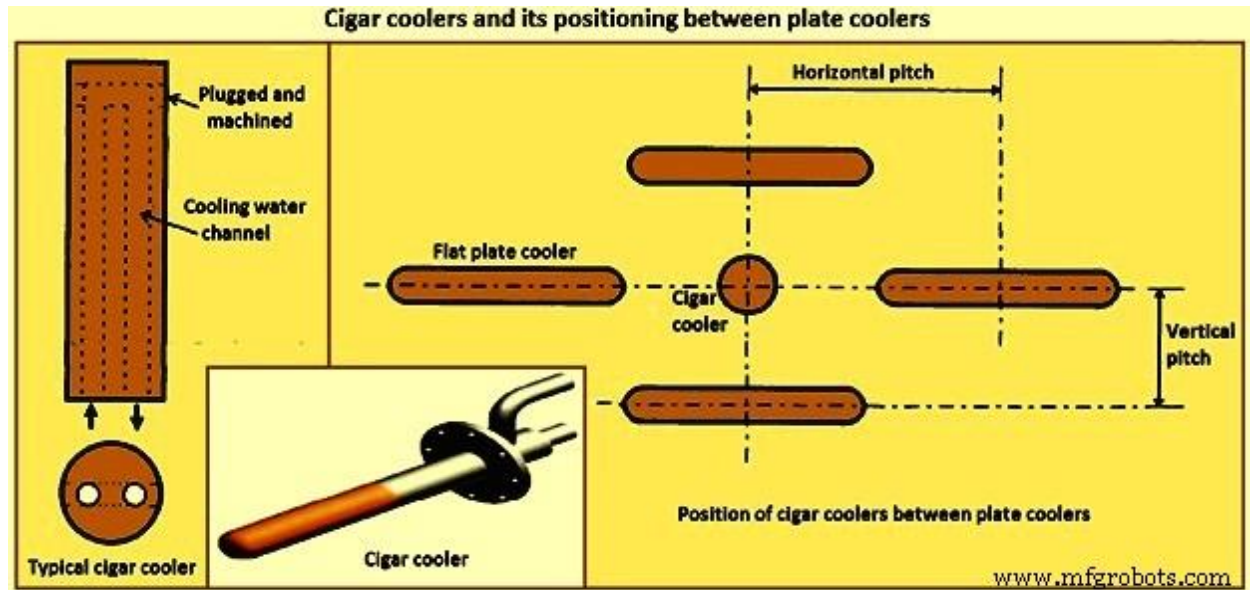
Сигарний охолоджувач і його розташування між пластинчастими охолоджувачами
